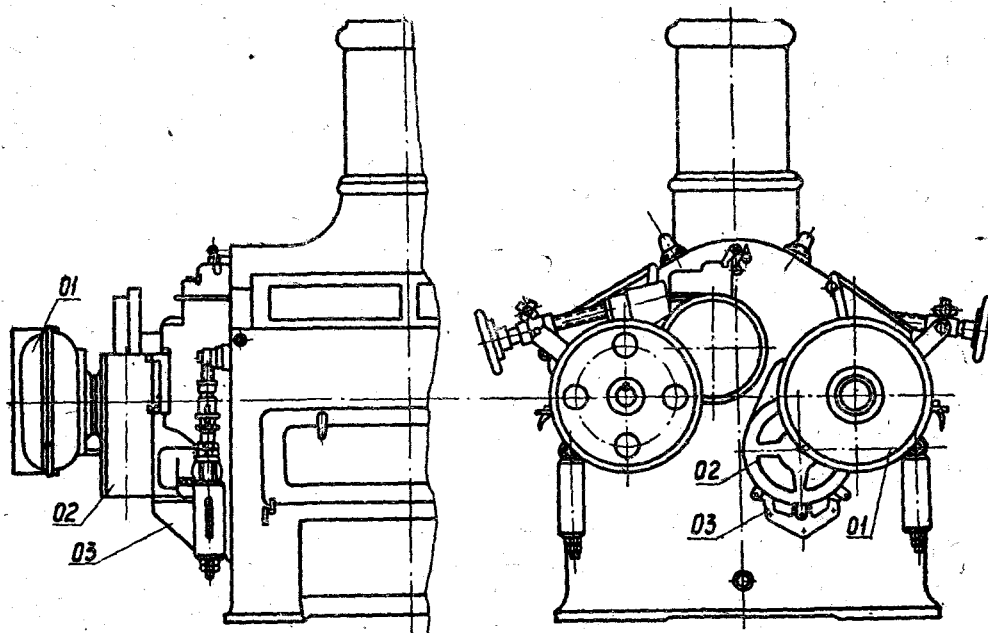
Общий вид вальцового станка, оборудованного межвальцовой гидротурбопередачей:
